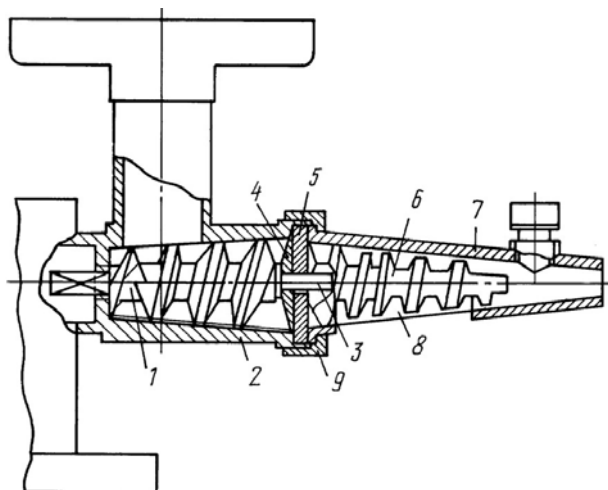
Шнековое устройство для извлечения сока из овощей и фруктов:
